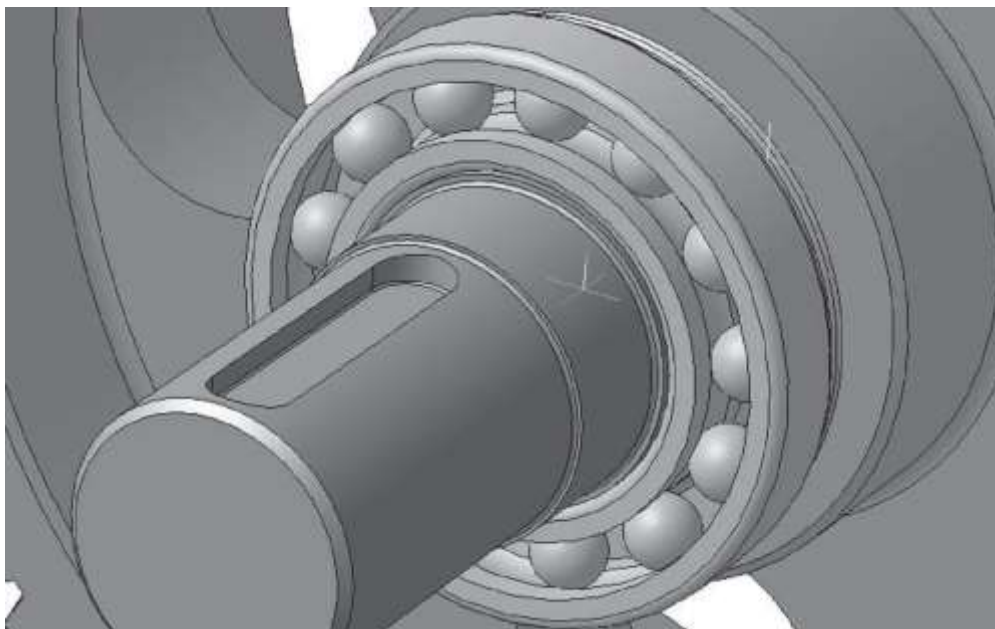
Підшипниковий вузол ведучого вала
